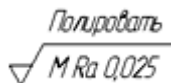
Обозначение метода обработки и допуска шероховатости поверхности детали
